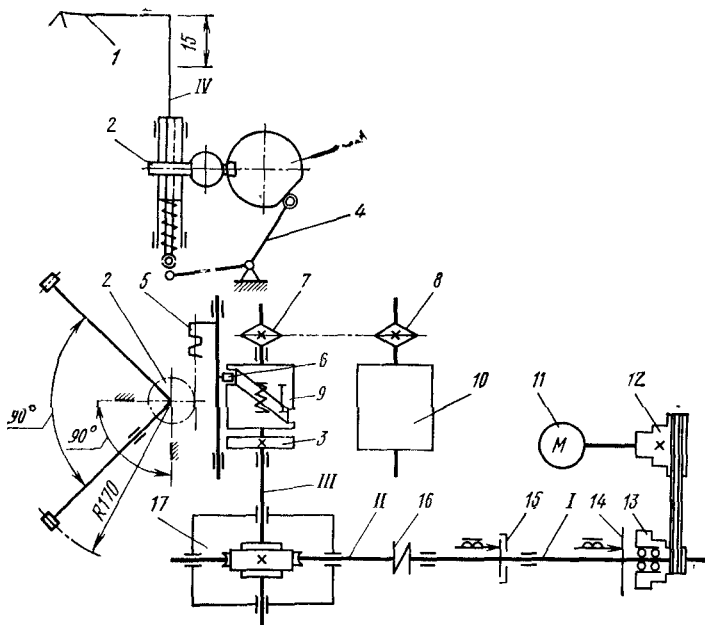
Кинематическая схема механической руки модели МР-12
